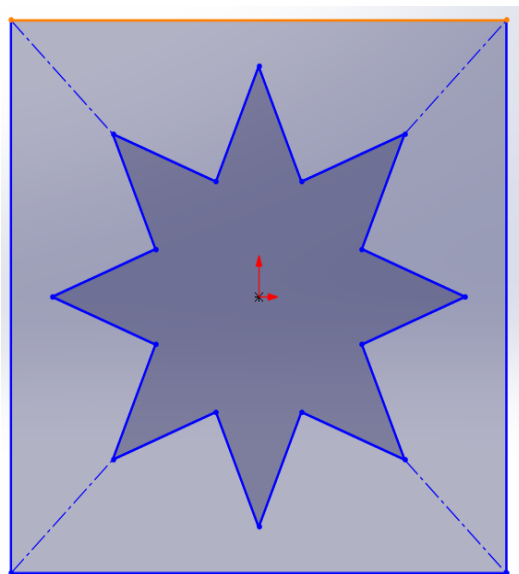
Croquis 4 Corte avanzado. Fuente: Creación propia
